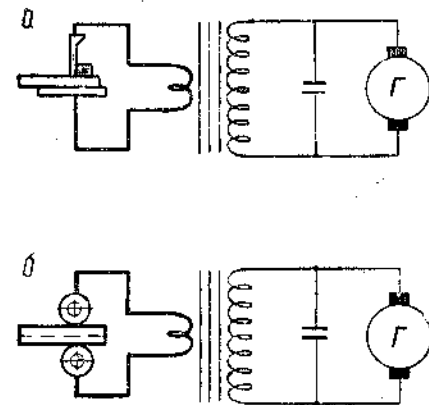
Схема промышленных способов сварки пластмасс токами высокой частоты:
